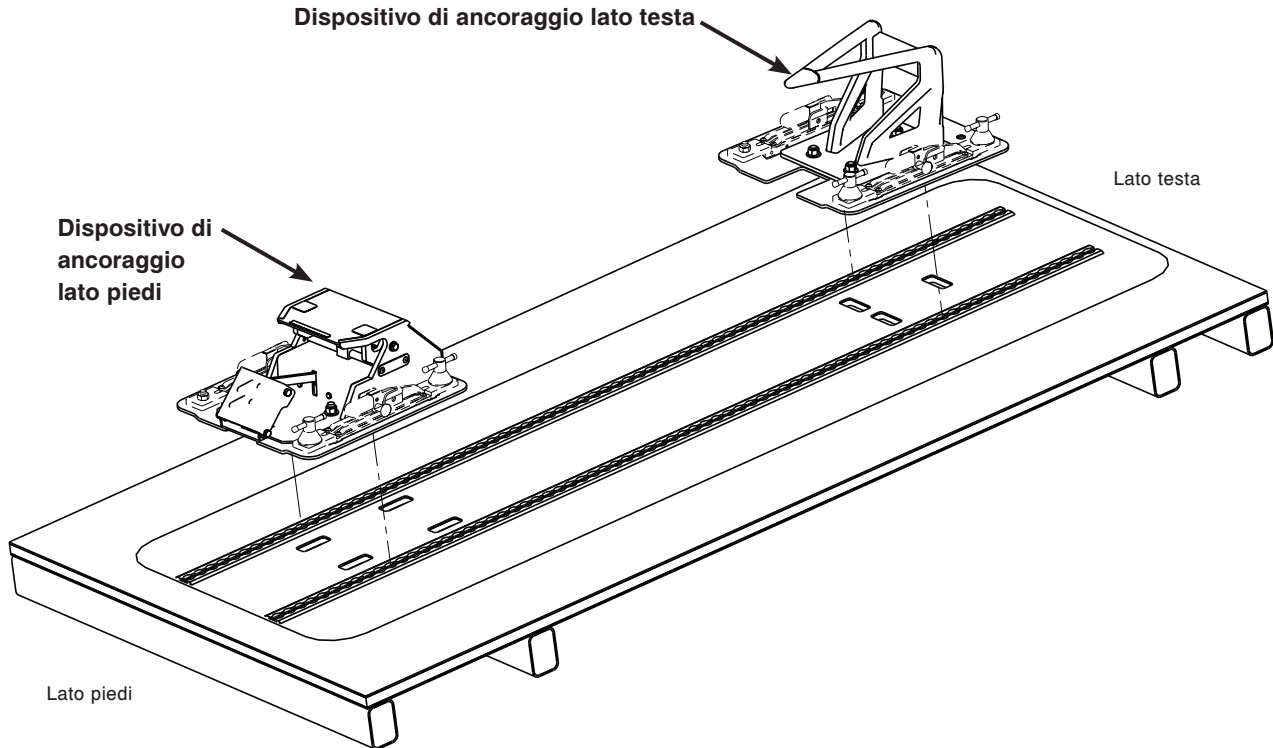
Dispositivi di ancoraggio per lato testa e il lato piedi – Installazione delle piste a pavimento
